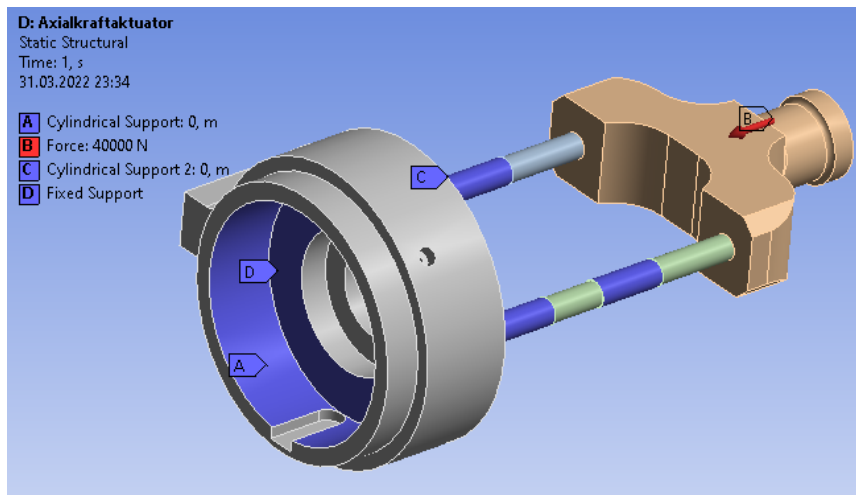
FEM Axialkraftaktuator - Kräfte und Lagerung
